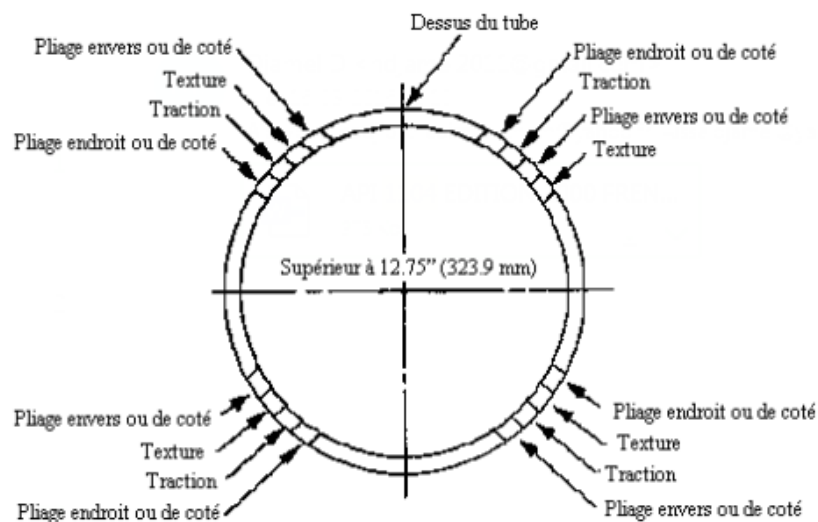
Emplacement des éprouvettes à soudure bout à bout pour l'essai de Qualification du mode opératoire
